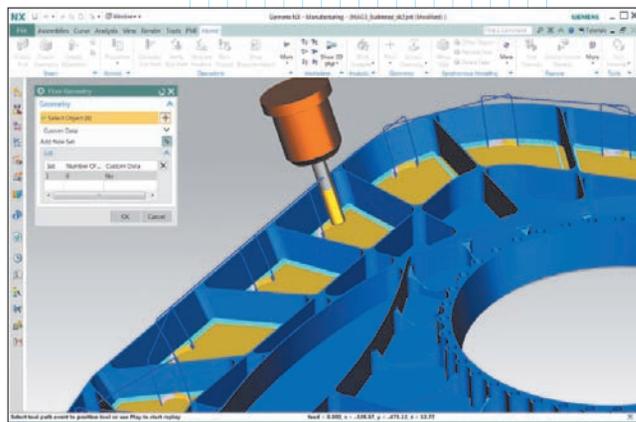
Комплексный автоматизированный процесс CAD-CAM-CNC позволяет получить максимальную выгоду от имеющегося оборудования
